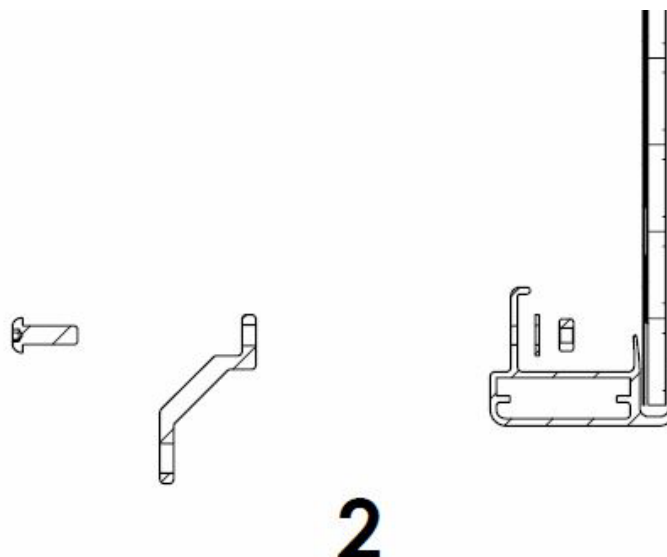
Detailansicht (Schnitt) zur Montage von zwei Wandhalterung Laschen
